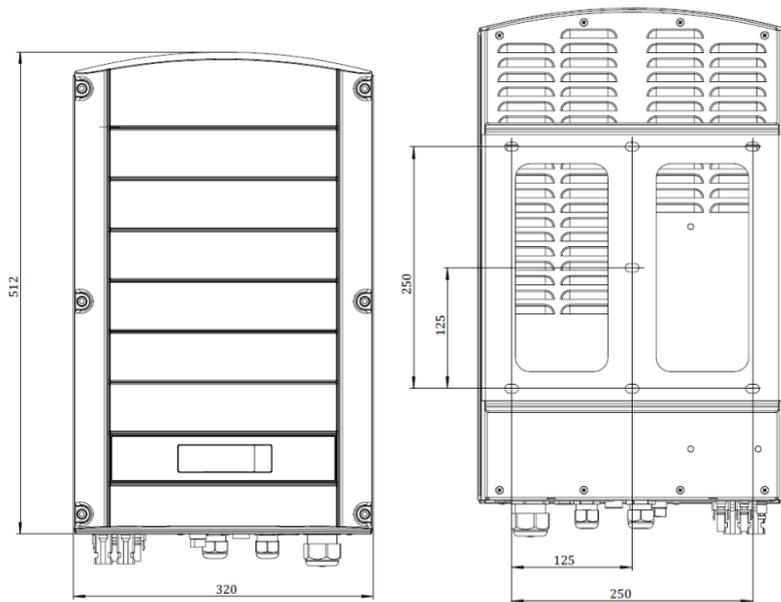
Onduleur triphasé avec un support de type 1 – Vue de face et arrière
